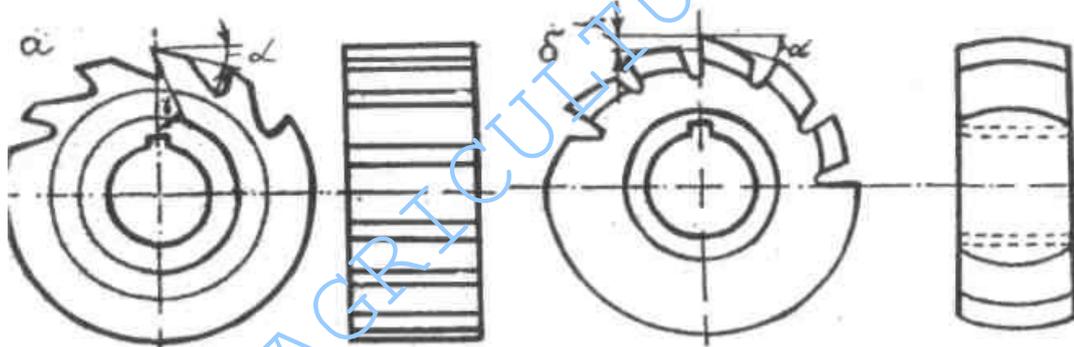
Схема фрезерования цилиндрической фрезой с обыкновенным (*а*) и затылованным (*б*) зубом
